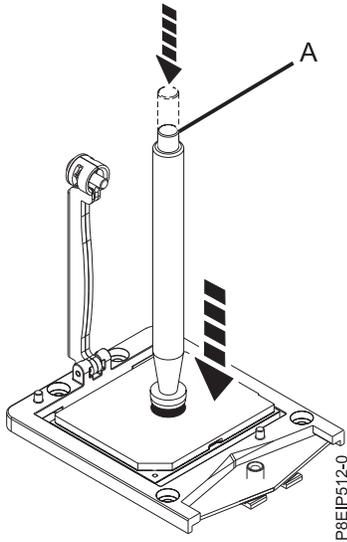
Ausbauwerkzeug auf das Systemprozessormodul herabsenken
